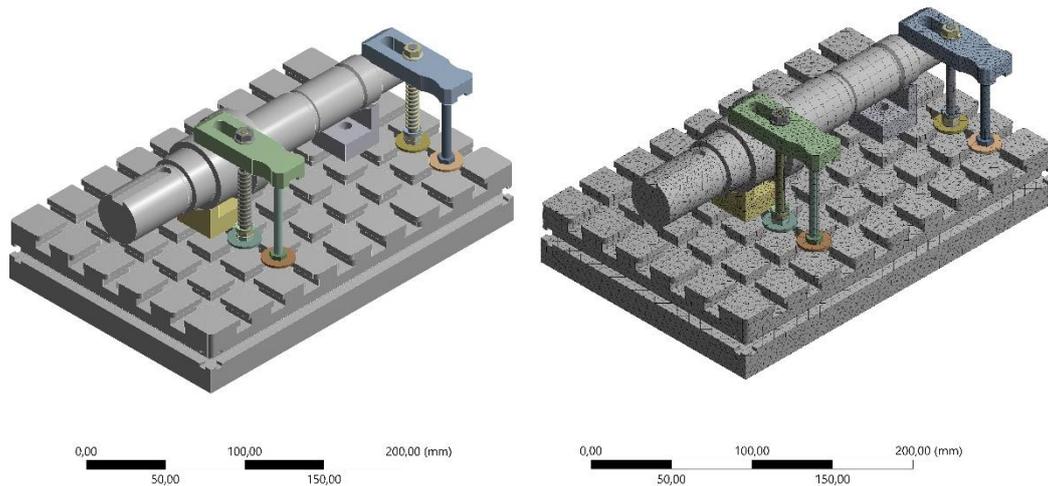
Геометрическая и конечно-элементная модель станочного приспособления в сборе с обрабатываемой деталью
